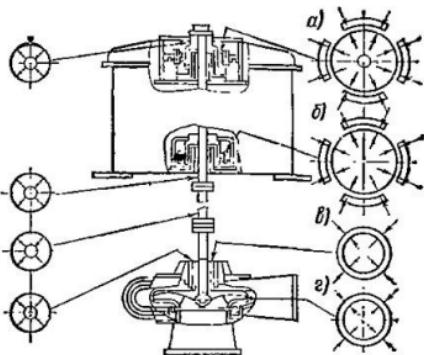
Места проверки биения вала индикаторами и проверяемых зазоров
